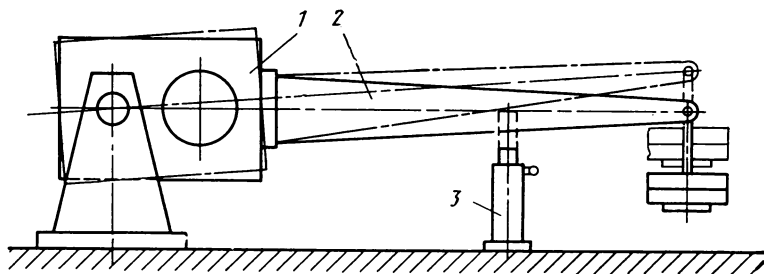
Схема приспособления, имитирующего реверсивный режим работы шлицевого соединения
